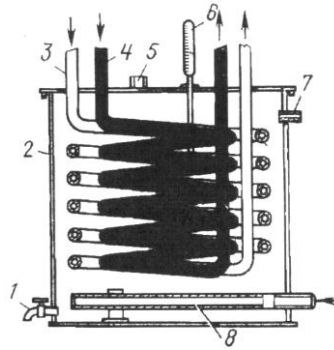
Принципова схема лакопідігрівача: 1 - зливний кран; 2 - бак; 3 - труба для повітря; 4 - труба для лаку; 5 - заливна труба для води; 6 - термометр; 7 - патрубок для видалення пари; 8 - колектор для подавання пари
